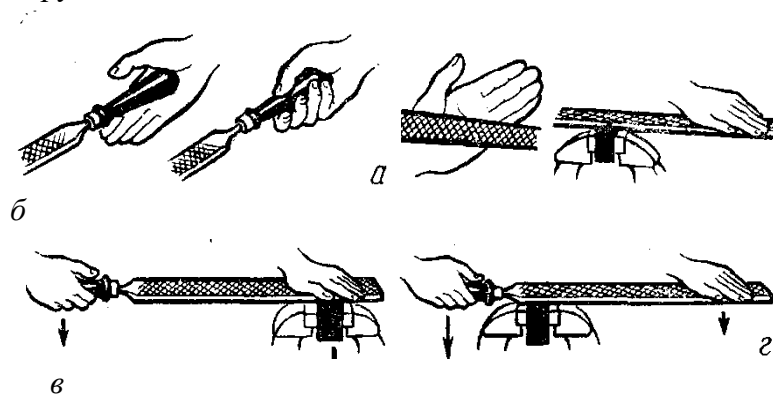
Хватка напильника и балансировка им в процессе опиливания:
